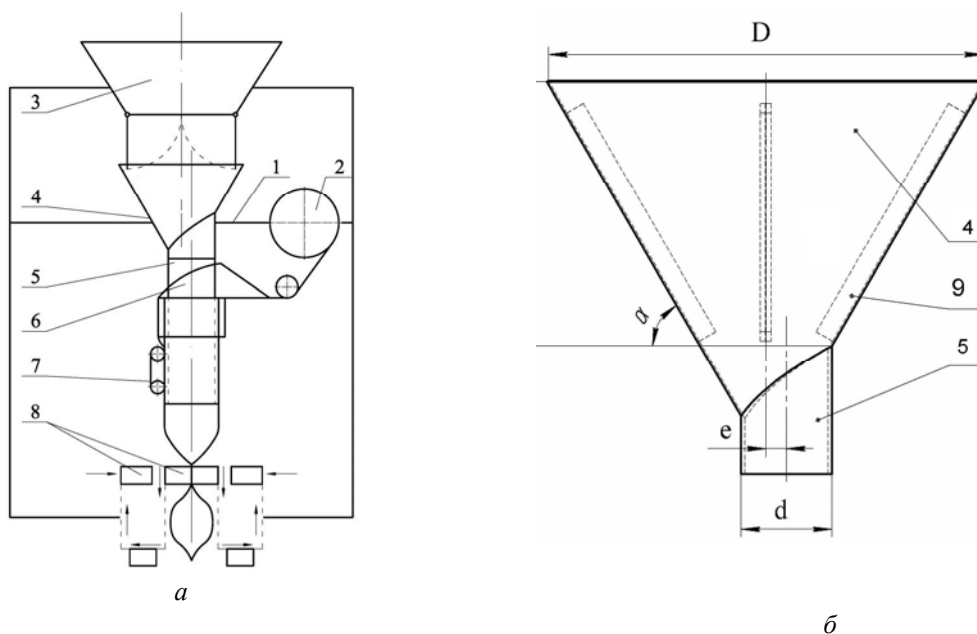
Схема роботи пакувального автомата неперервної дії: 1 – пакувальний автомат; 2 – плівка; 3 – дозатор; 4 – приймальна лійка; 5 – тубус; 6 – формувальний комір; 7 – механізм зварювання поздовжнього шва; 8 – зварні колодки поперечного шва; 9 – напрямні планки
